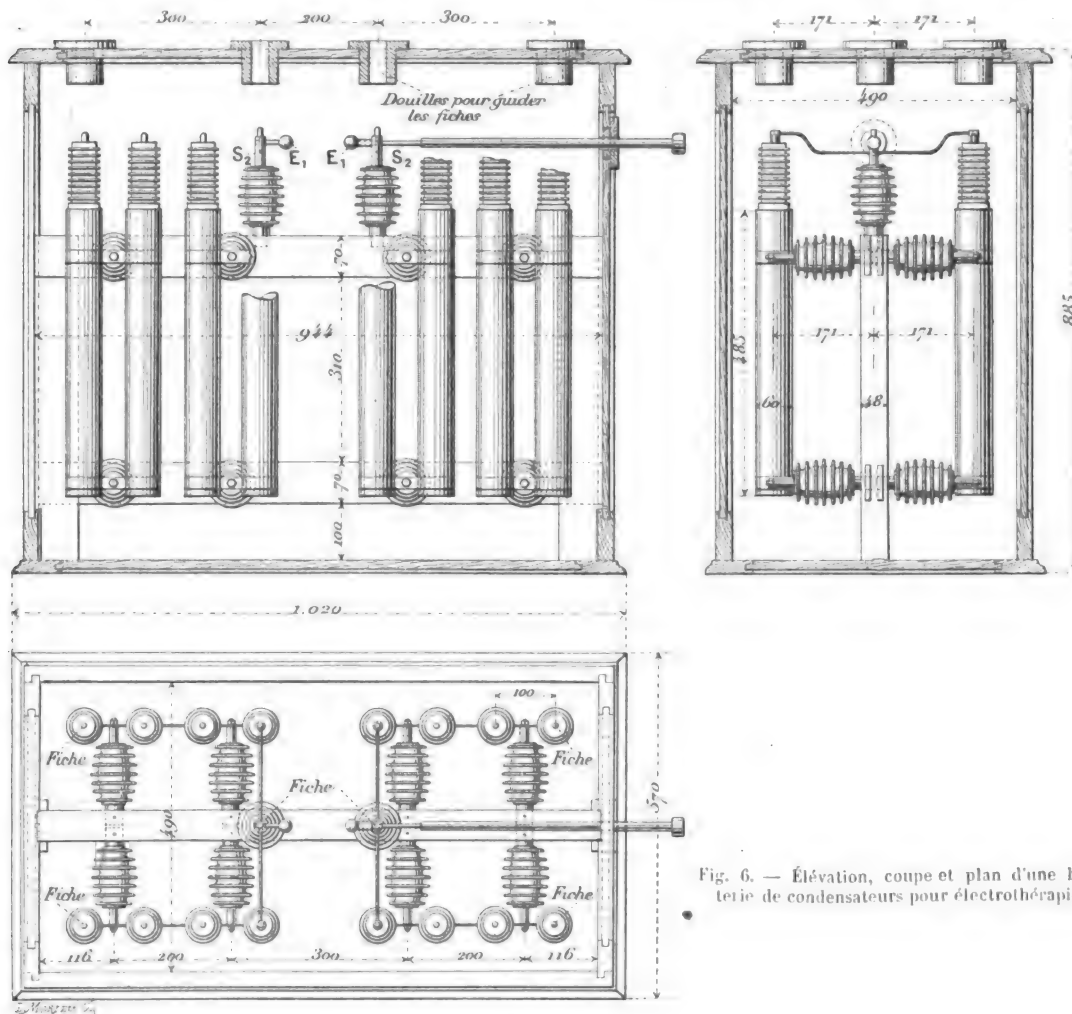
Élévation, coupe et plan d'une batterie de condensateurs pour électrothérapie
